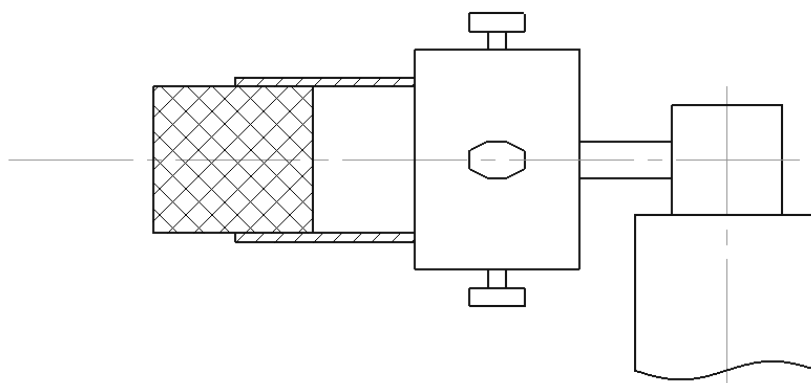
Установка изготовленного центратора в свариваемое изделие
